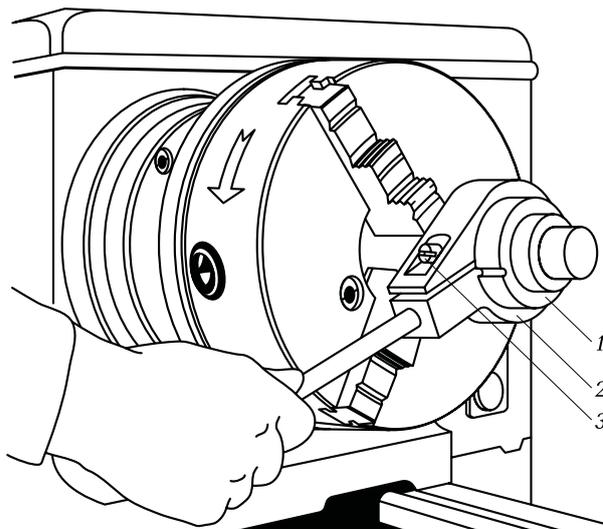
Притирка наружной цилиндрической поверхности:
